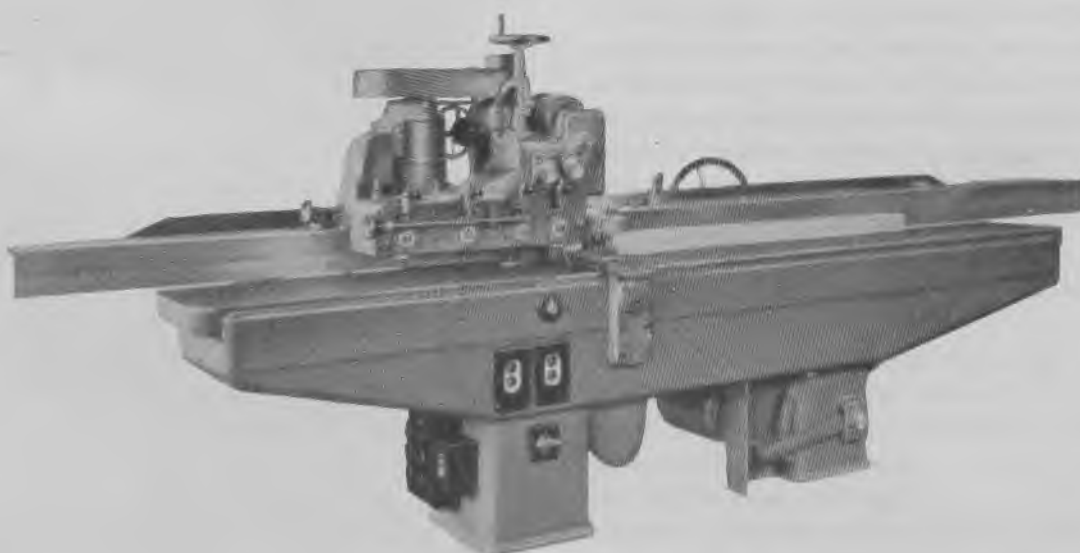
To-sidet afretter. Sidekutteren er anbragt bagved den horisontale høvkutter og går ned i en udfræsning i det bageste bord. Maskinen er desuden forsynet med fremføringsapparat. Fremføringshastighed: 7,5-20 m/min.
